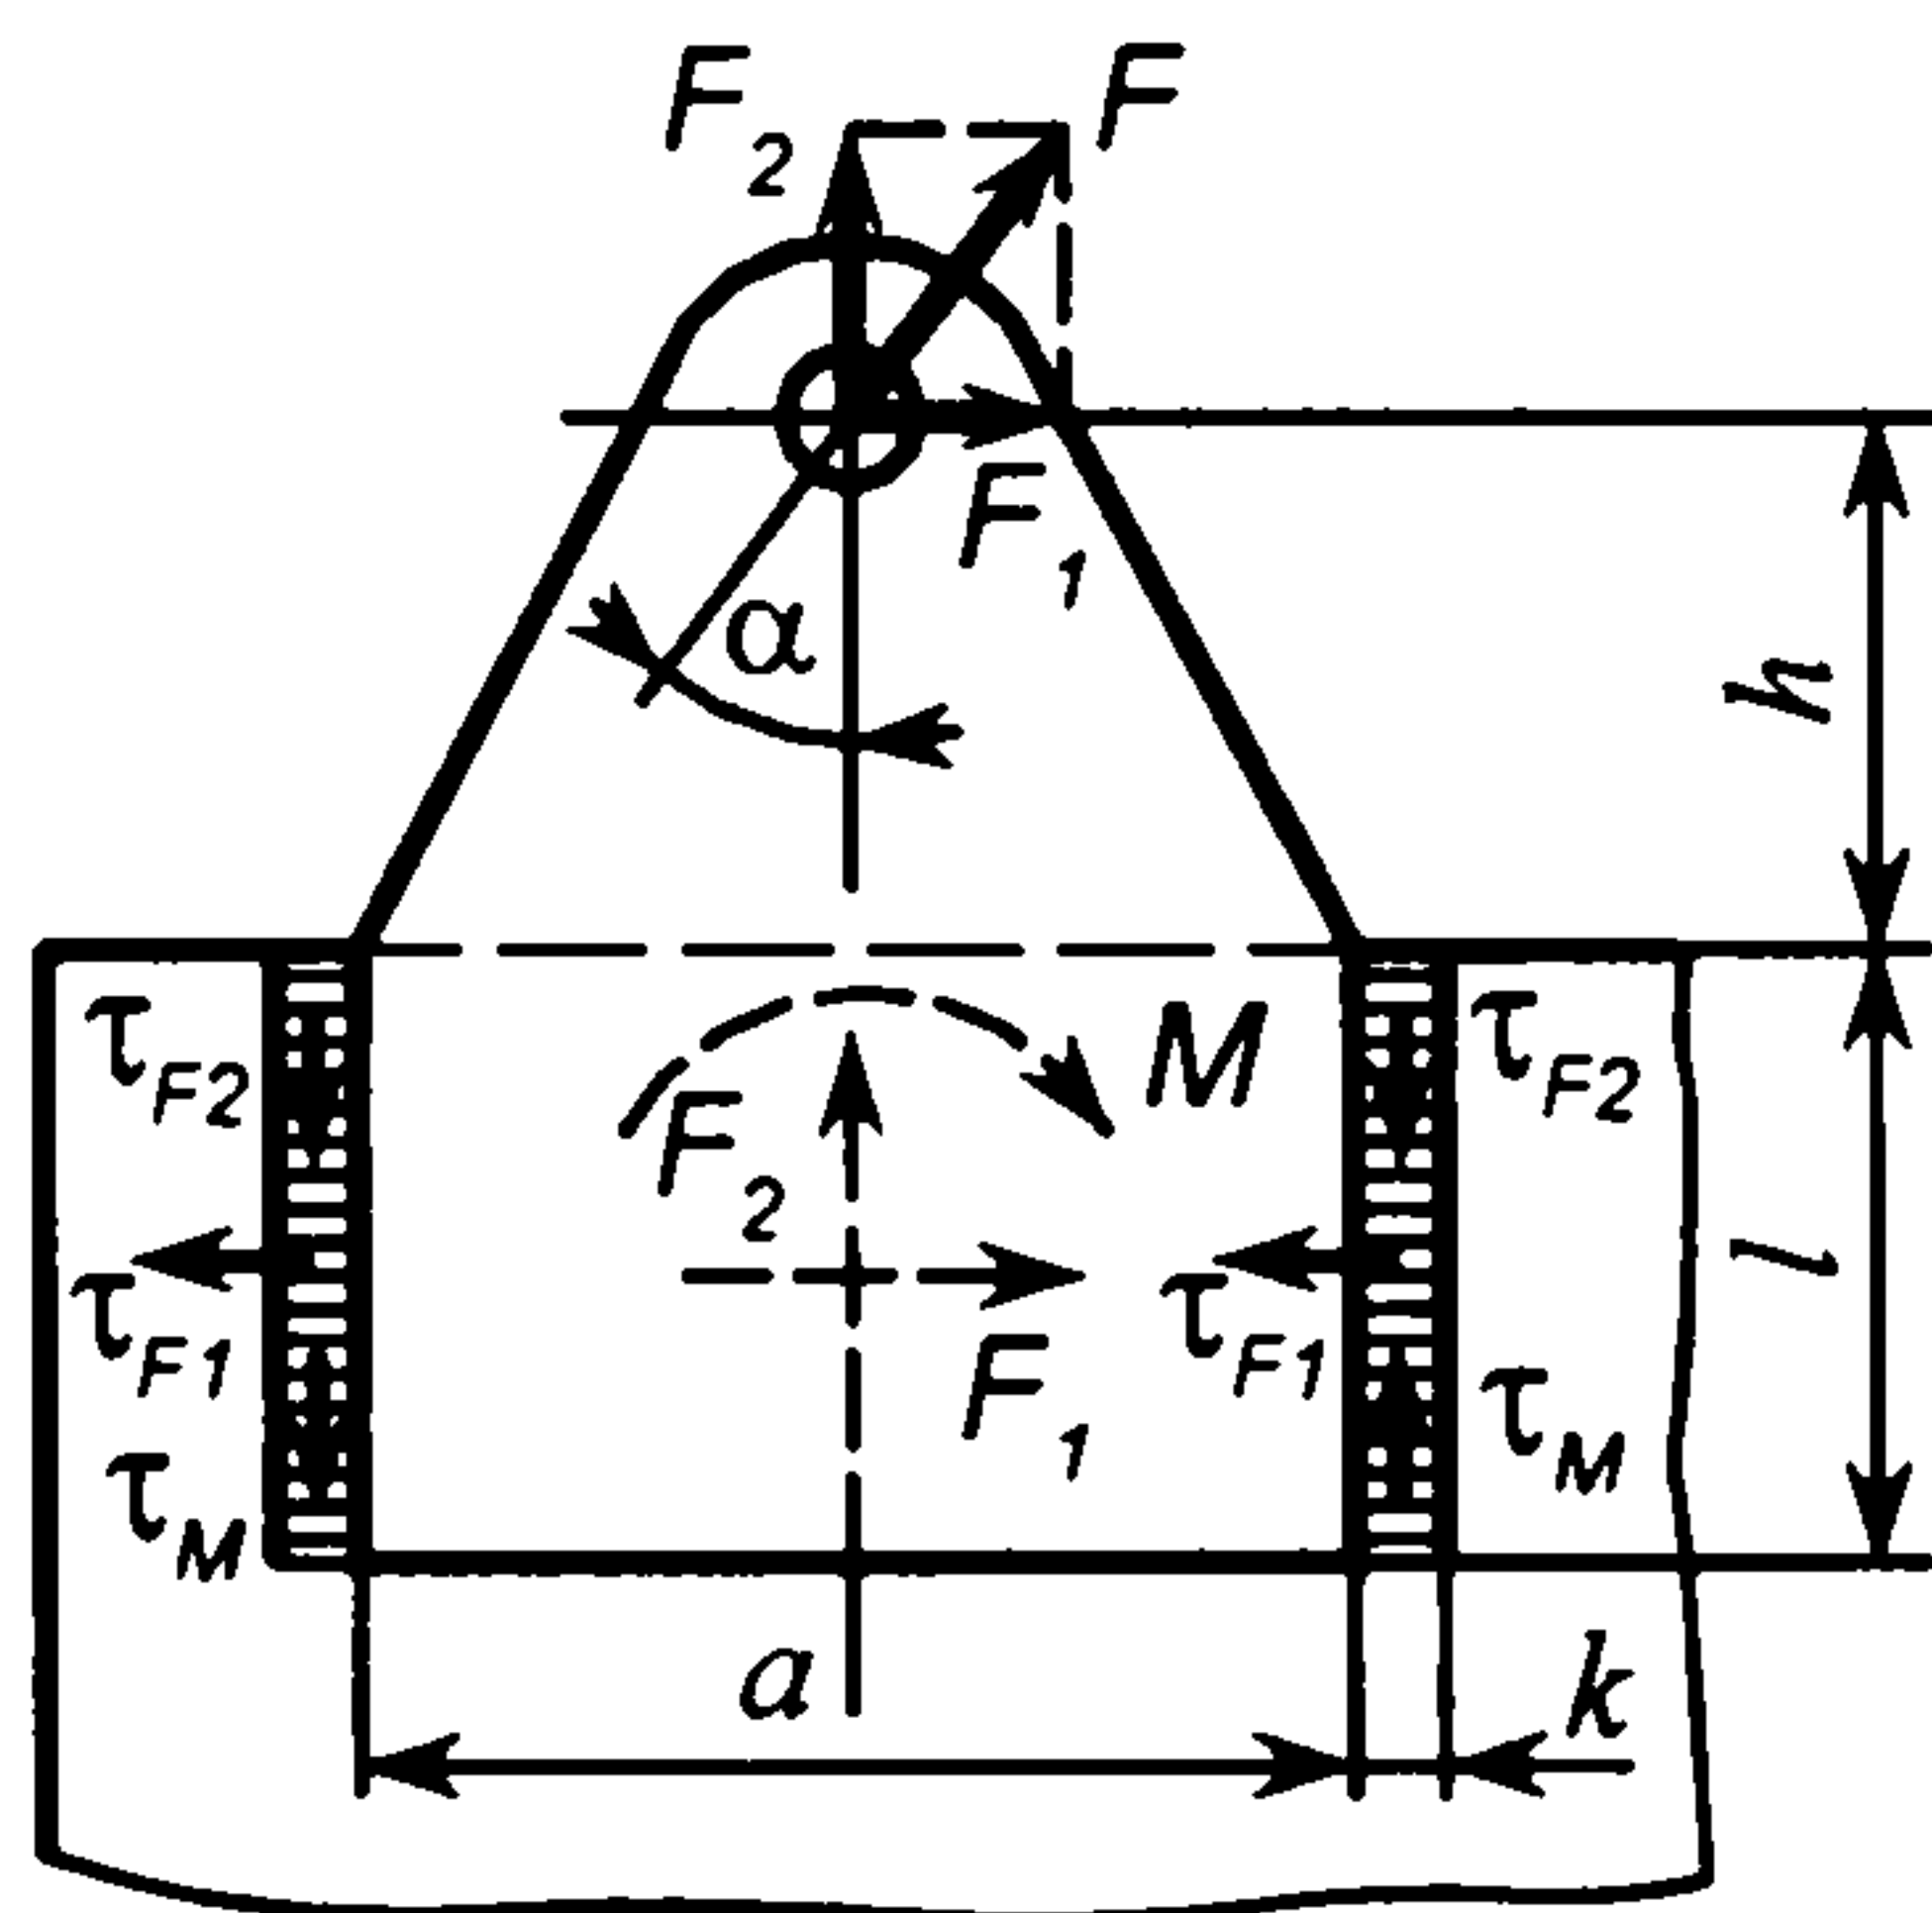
Зварне з'єднання кронштейна з корпусом
